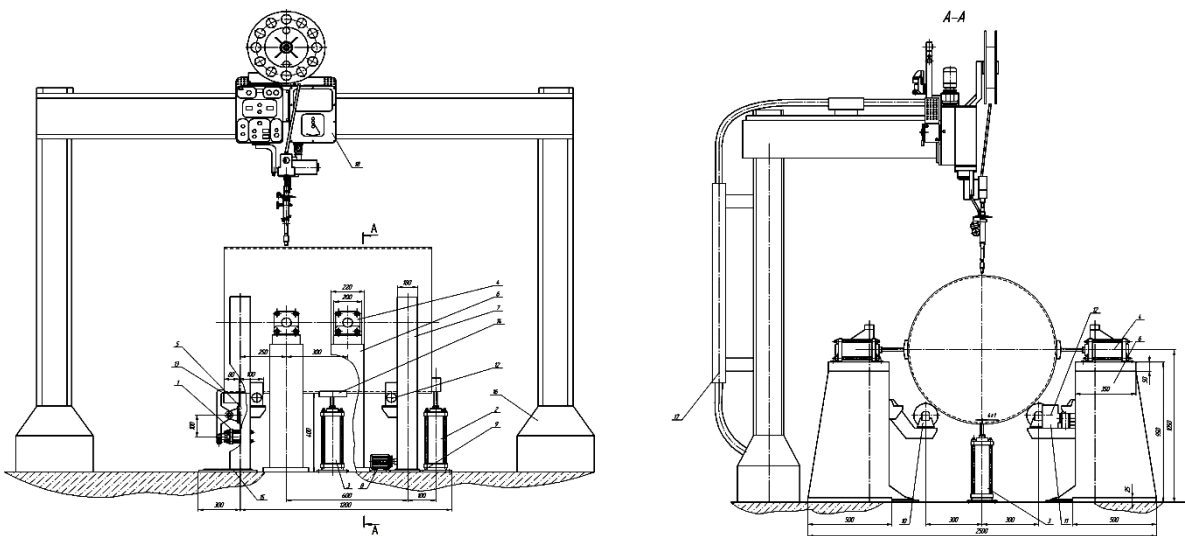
Установка для складання і автоматичного зварювання обичайки
